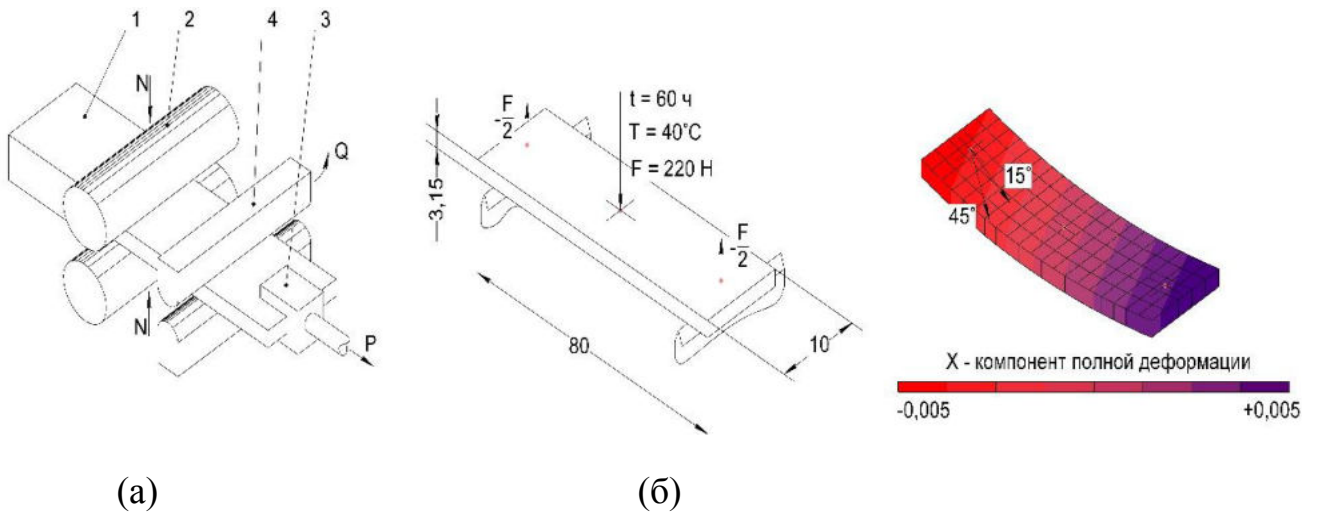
Схема (а) получения лигатурной пластины Al–Mg–SiC в валках-кристаллизаторах: 1 – жидко-твердый расплав, 2 – валок-кристаллизатор; 3 – механизм протяжки; 4 – формирование заготовки; (б) заготовка
